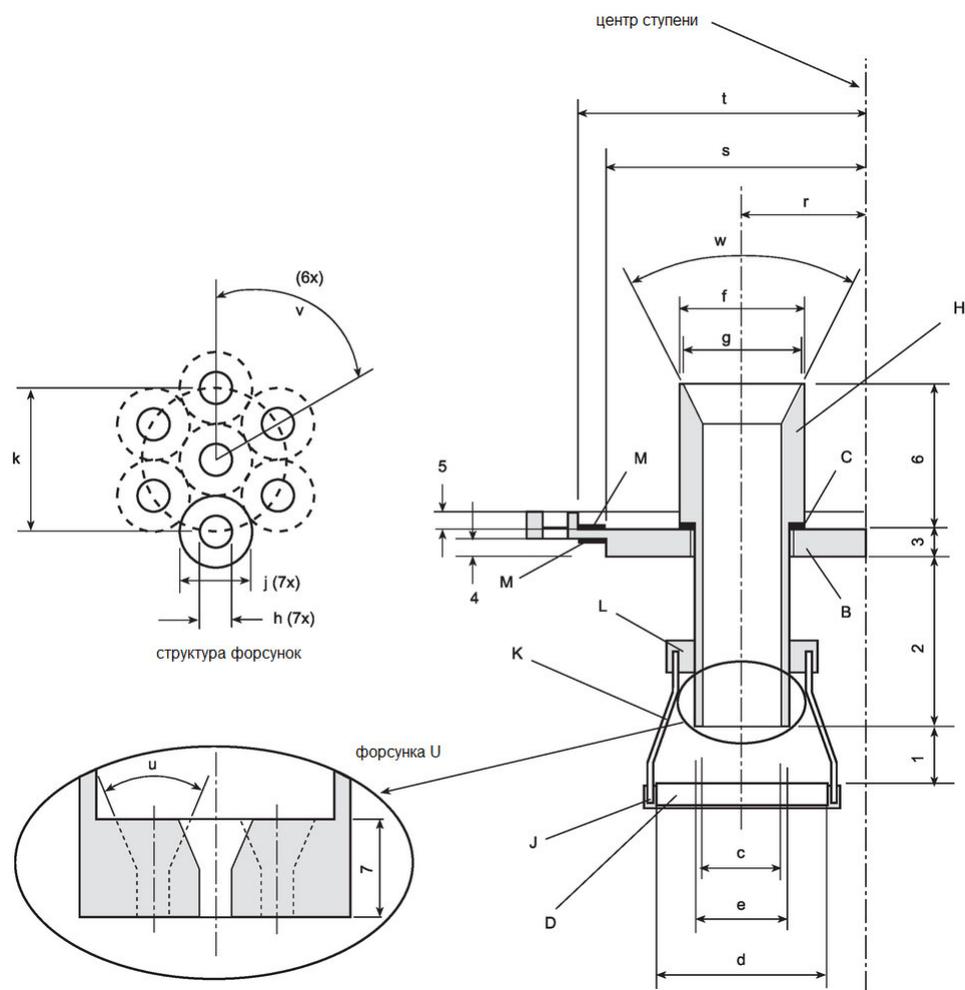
Прибор С: детали распылительной трубки и импакторной пластины
